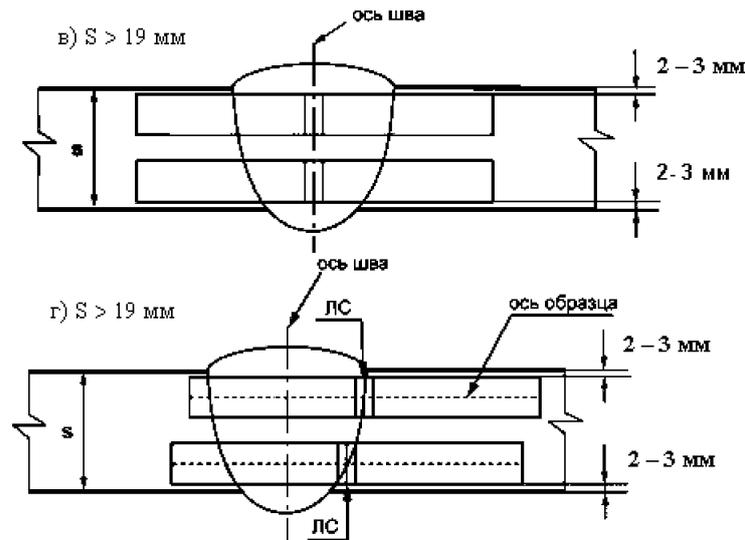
Форма и размеры образцов для испытаний на ударный изгиб по ГОСТ 6996-66
